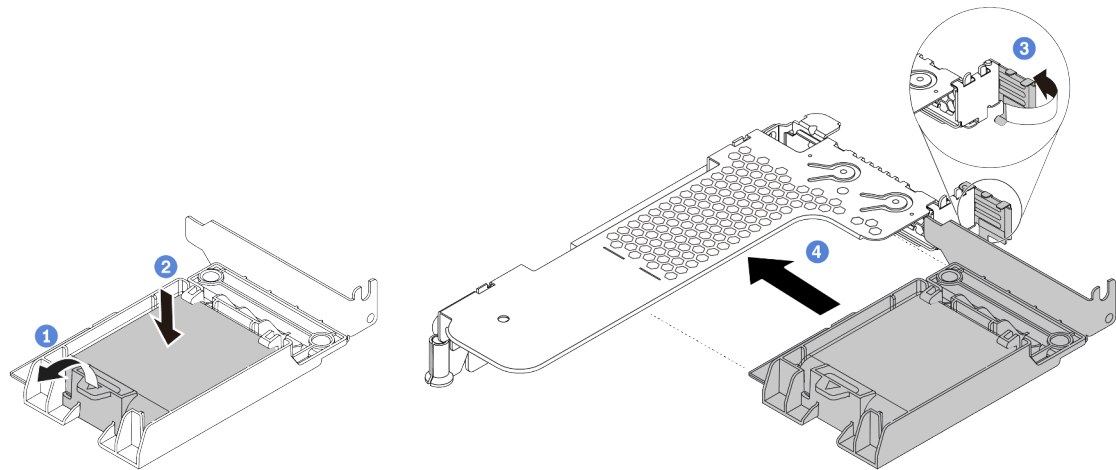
Installation du module d’alimentation flash RAID sur la carte mezzanine
